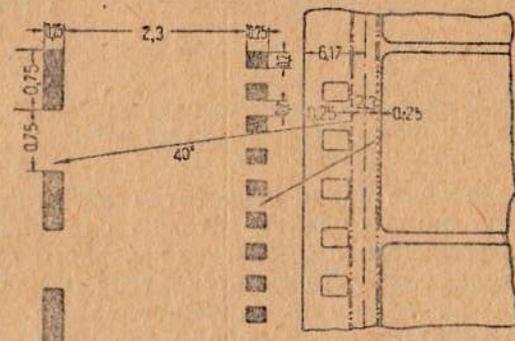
Контрольный фильм для установки оптической щели по фонограмме.
